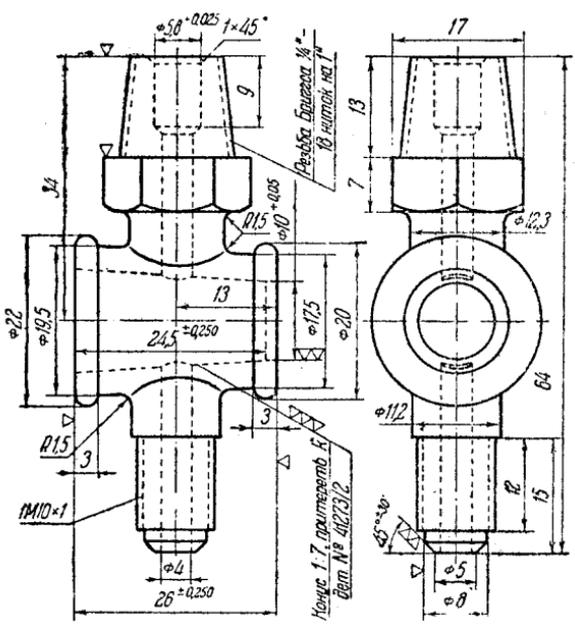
Дет. № 41273/1. Корпус проходного краника
